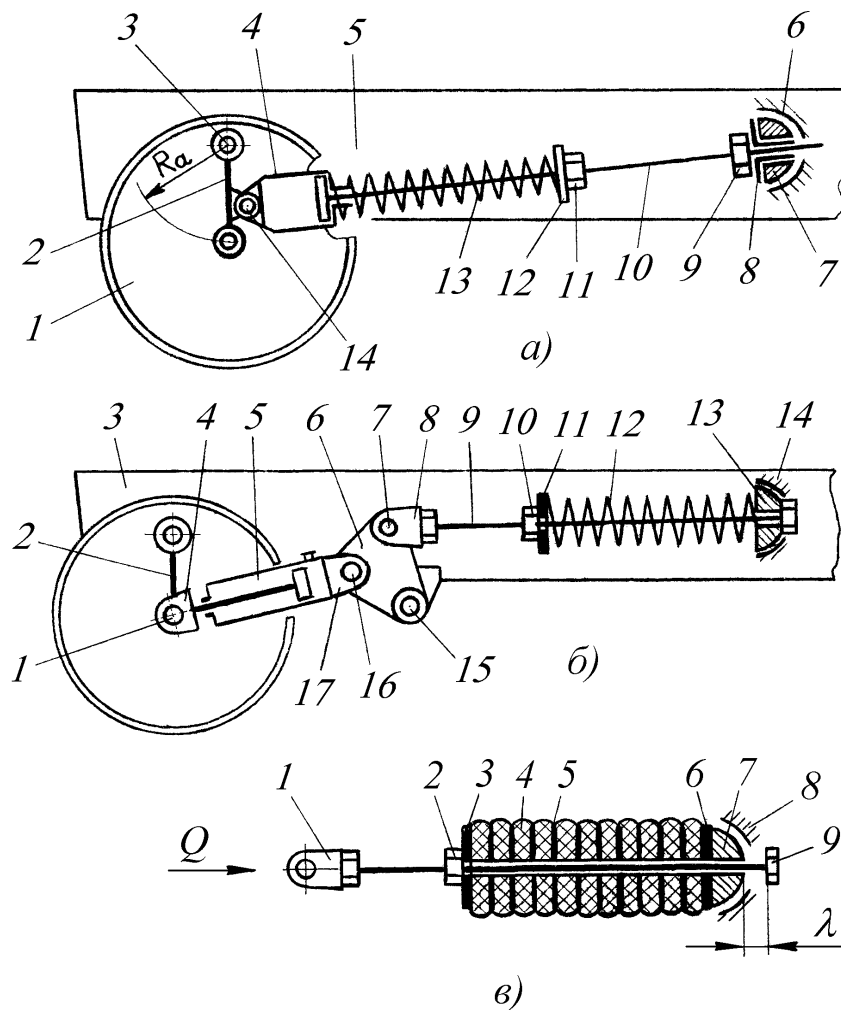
Принципиальные схемы конструкций натяжного и амортизирующего устройств, устанавливаемых на раме трактора
